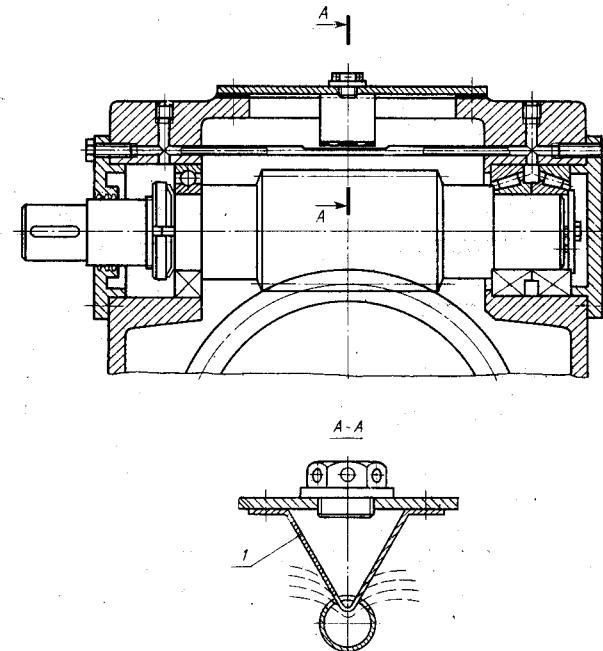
Смазывание подшипников через маслосборную трубку
